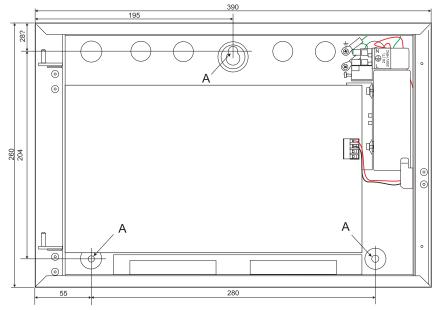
Dimensiones y puntos de fijación - cabina pequeña
